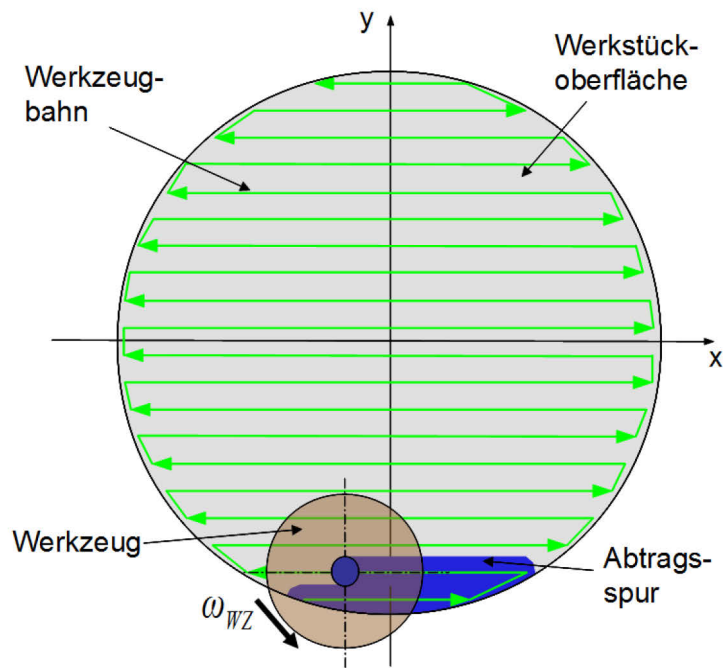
Skizze der Politur eines festen Werkstücks, das braun unterlegte Werkzeug dreht sich um seine Achse und bearbeitet das Werkstück in einer rasterförmigen Werkzeugbahn. Die blaue Kontaktfläche im Zentrum des Werkstücks erzeugt dadurch eine Abtragsspur.
